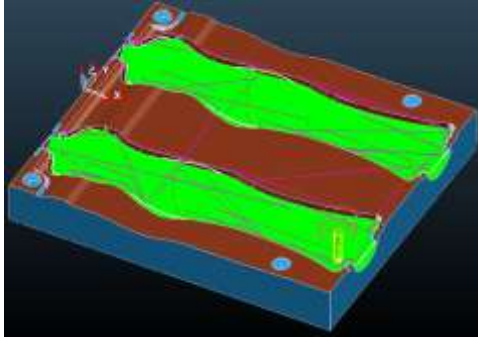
Траєкторія чистової обробки формуютьоючої поверхні першої напівформи
